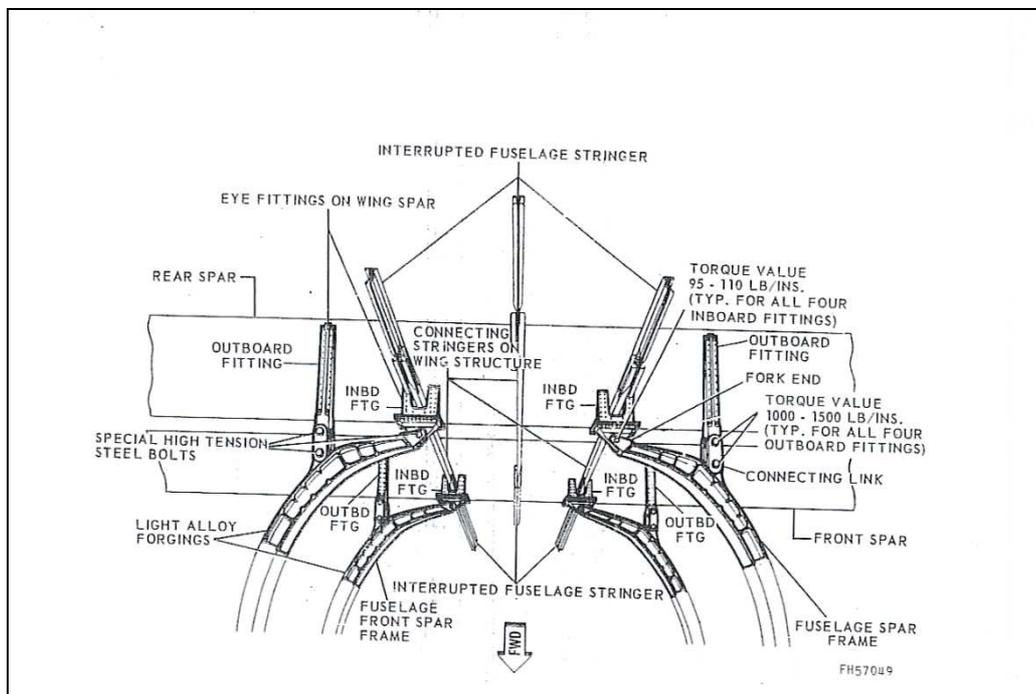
Wing Center Section to Fuselage Fittings
